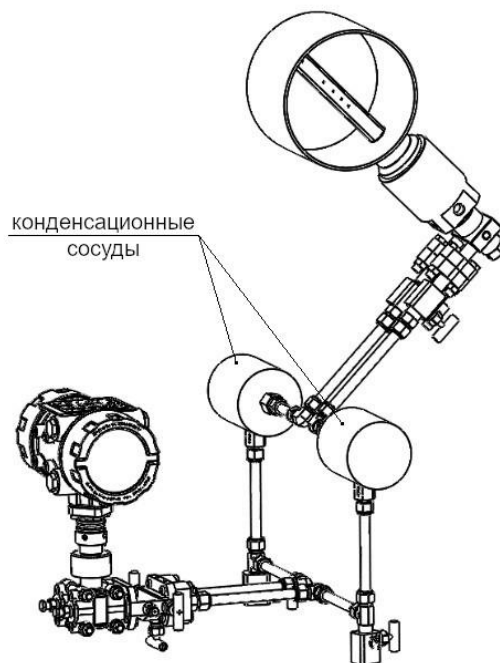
Расположение расходомера на трубопроводе выносной монтаж
